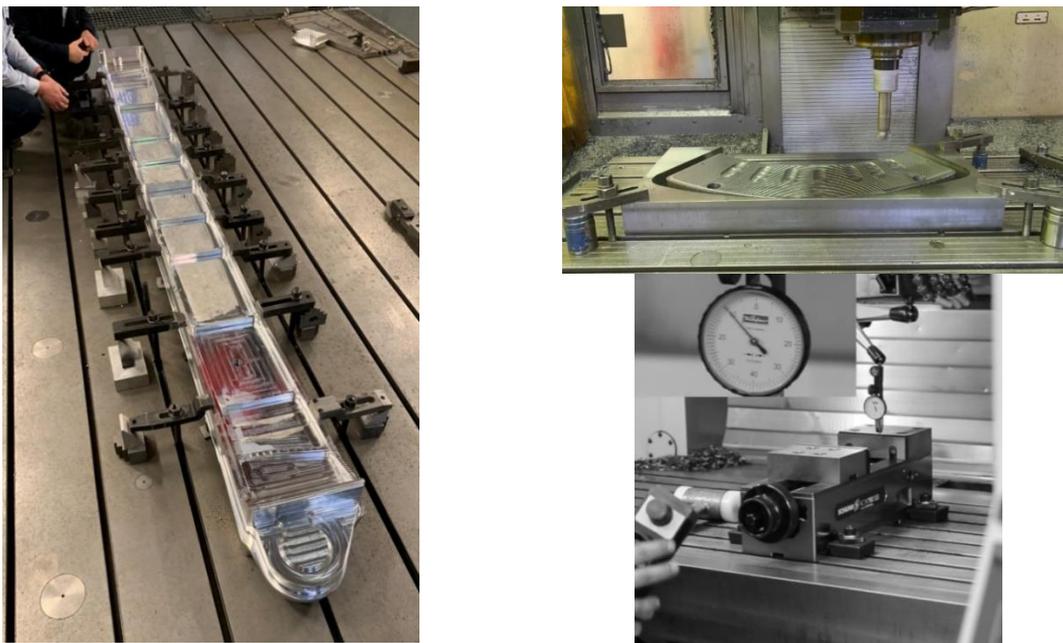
Традиционный вид крепления заготовок и приспособлений различной сложности и типов на станках фрезерной - расточной группы
